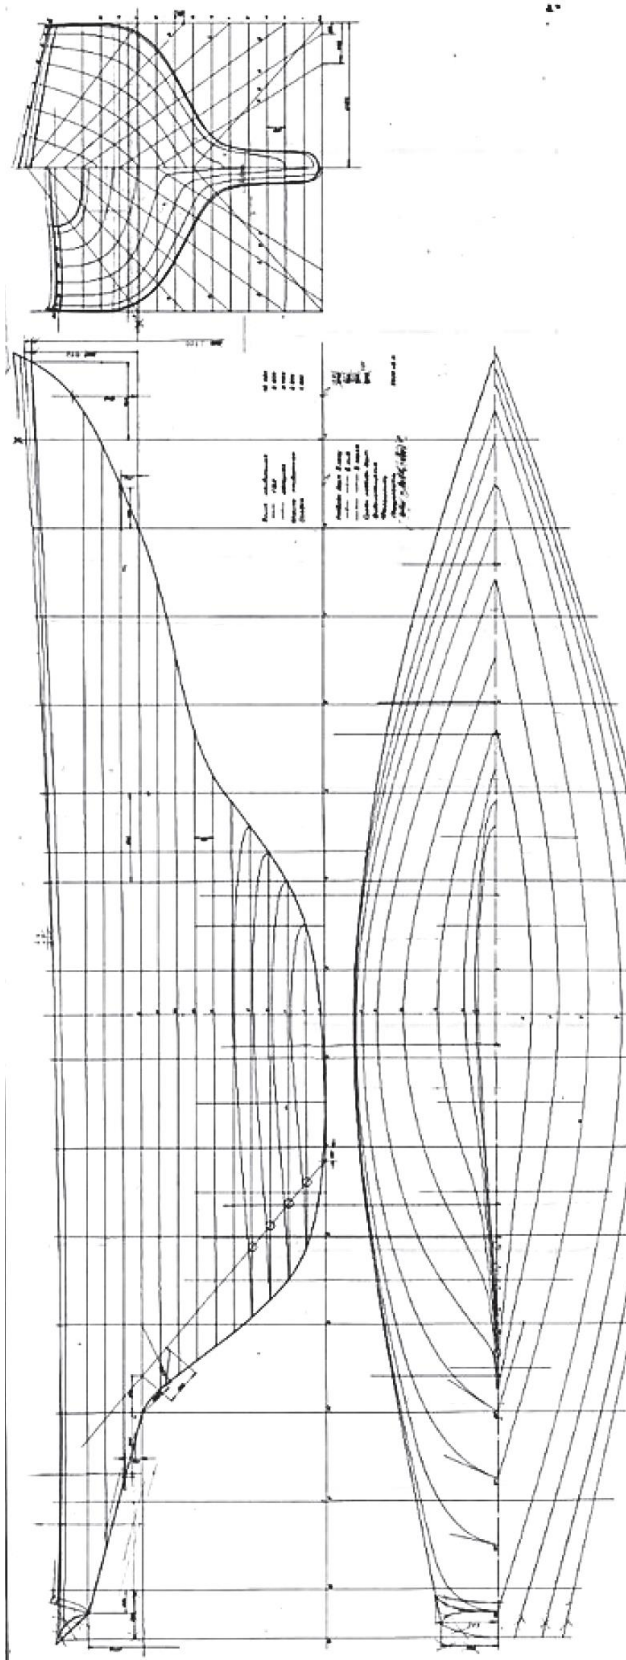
Теоретический чертеж и чертеж закладки яхты класса Л-6
